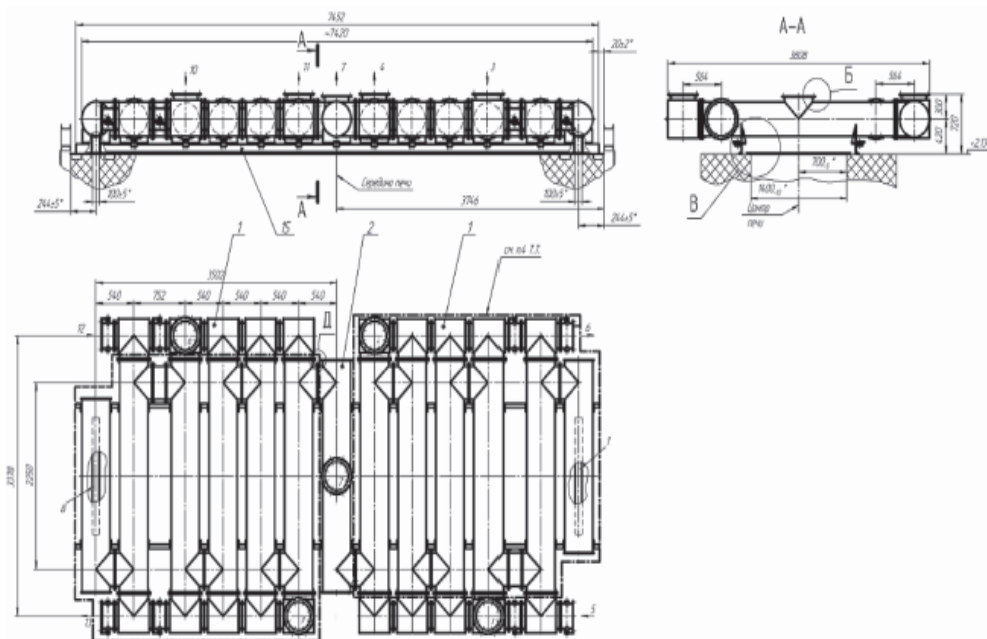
Трубчатый металлический рекуператор для нагревательной печи
